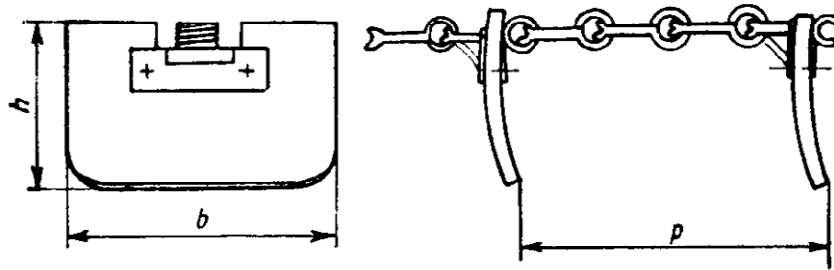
Construcția paletelor (raclete) montate pe lanț
